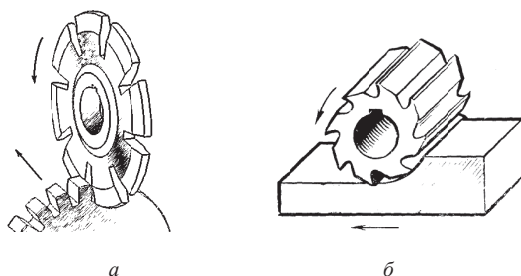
Схемы фрезерования: *а* – зубчатых колес дисковой модульной фрезой; *б* – поверхностей цилиндрической фрезой
